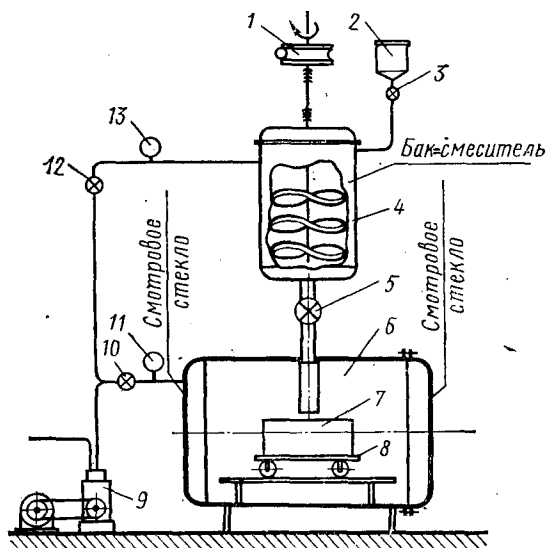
Схема установки для приготовления и заливки эпоксидного компаунда
